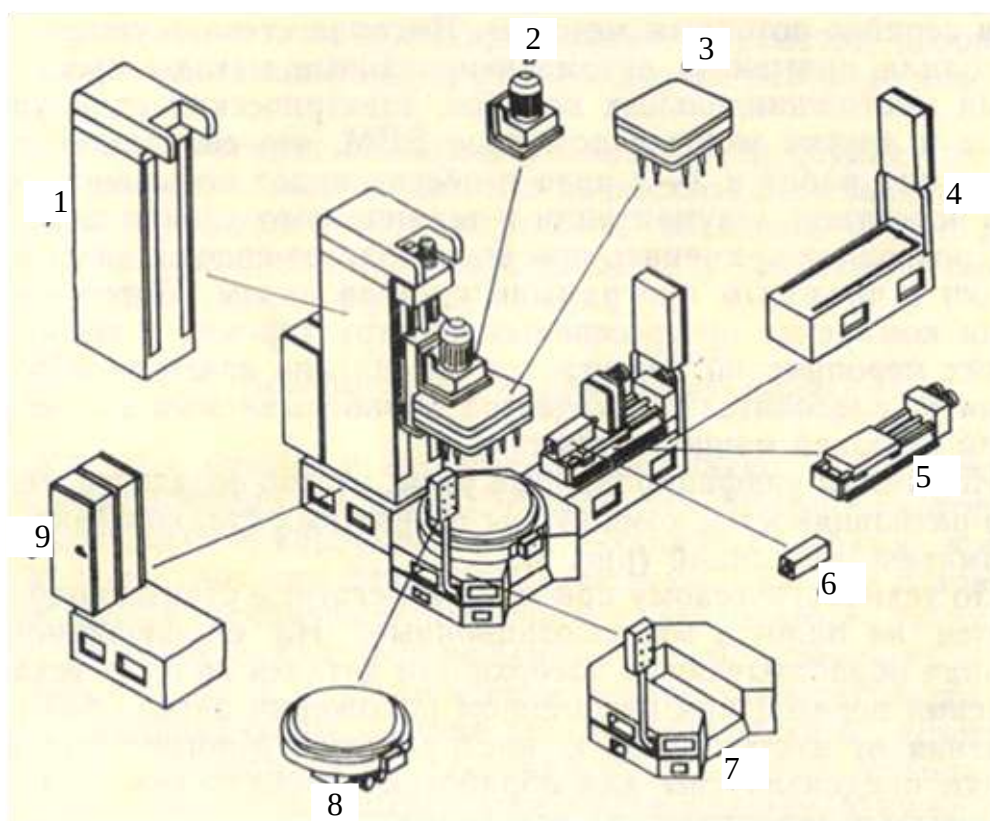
Схема компоновки агрегатного станка: 1 – стойка; 2 – силовая бабка; 3 – многшпindleная коробка; 4 – станина боковая; 5 – самодействующий силовой стол; 6 – одношпindleная расточная бабка; 7 – станина центральная; 8 – поворотный делительный стол; 9 – станина-подставка
